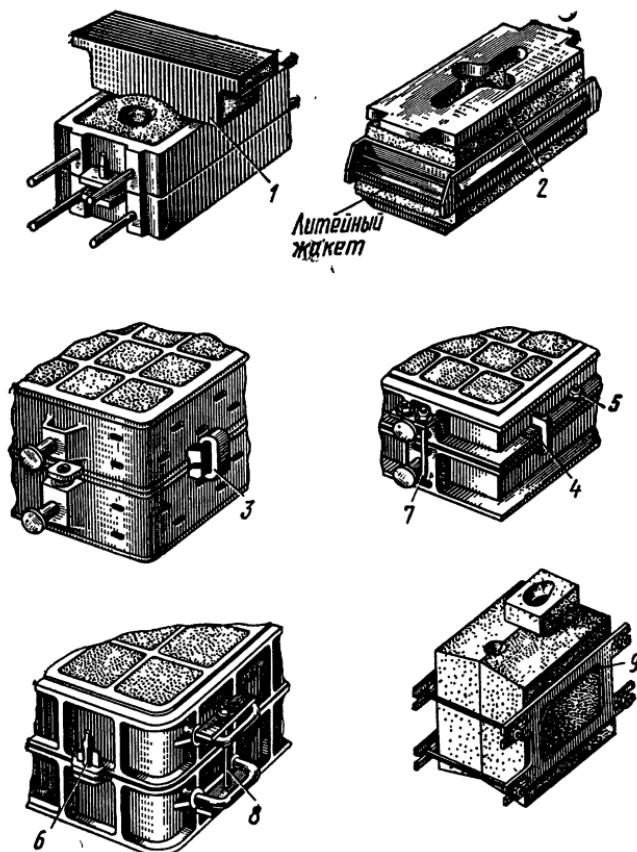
Способы скрепления полуформ перед заливкой:
